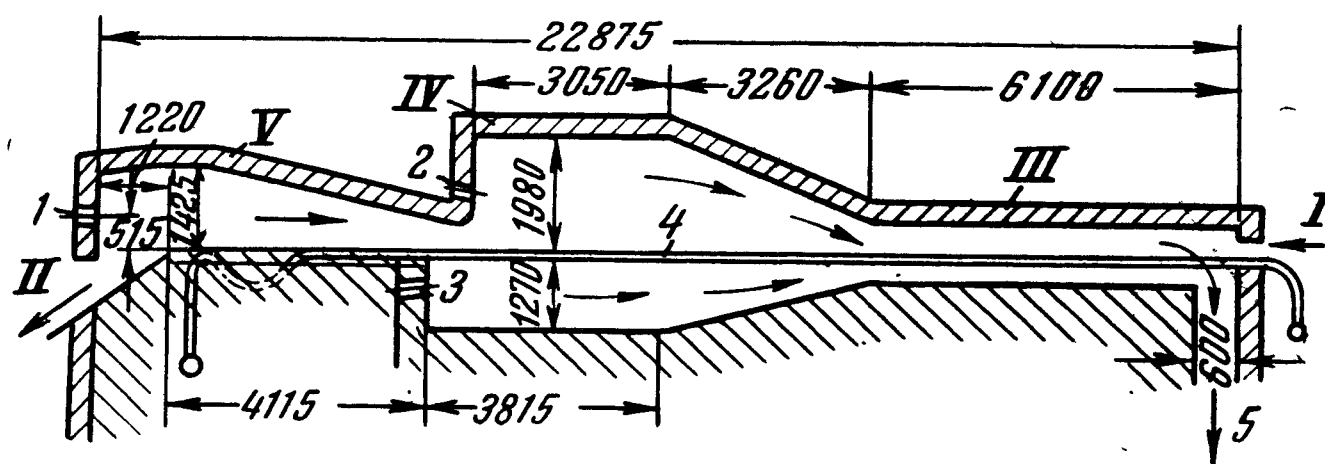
Схема методической печи для двустороннего нагрева заготовок.
